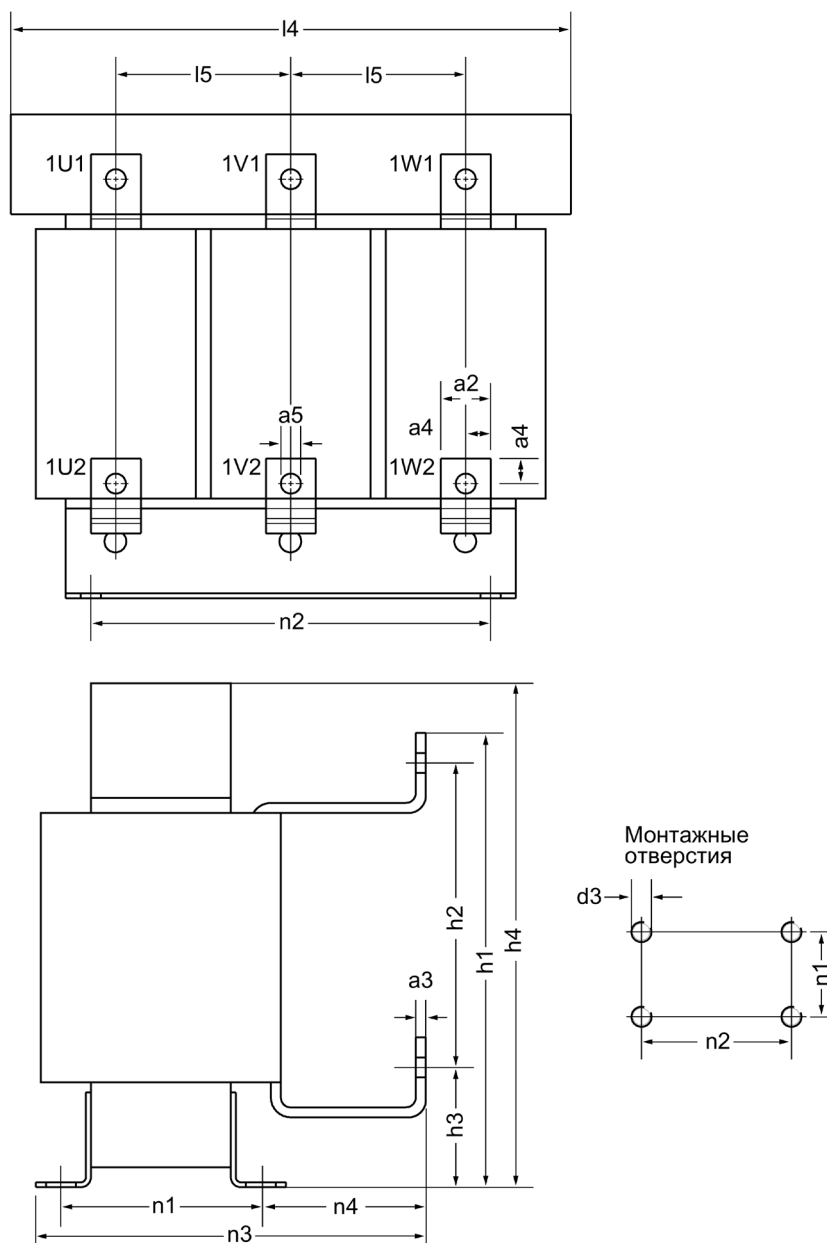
Габаритный чертеж сетевого дросселя
